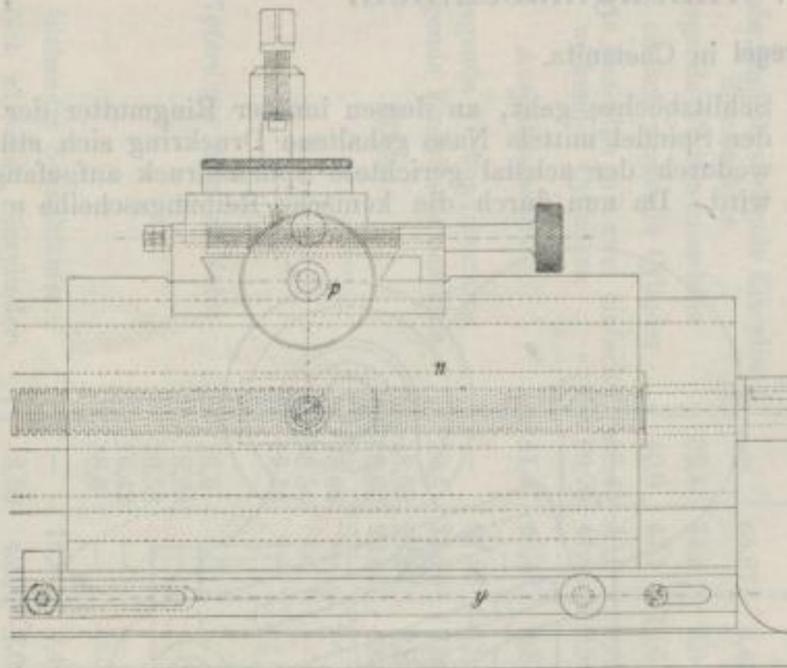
Drehbank für Gewindebohrer, Bolzen und ähnliche Werkzeuge.
